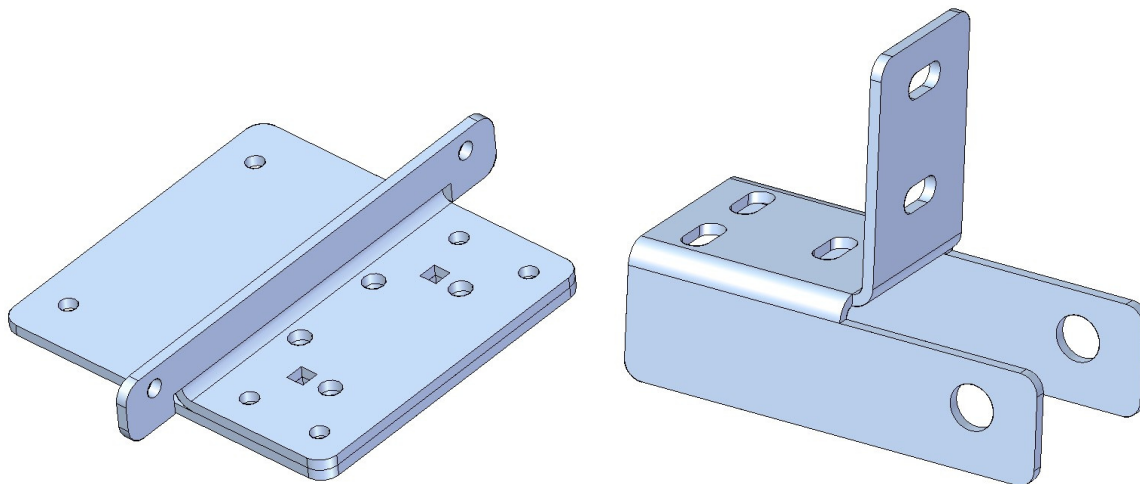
Fönsterkonsoler: a) WRG-1, b) WRD-1
